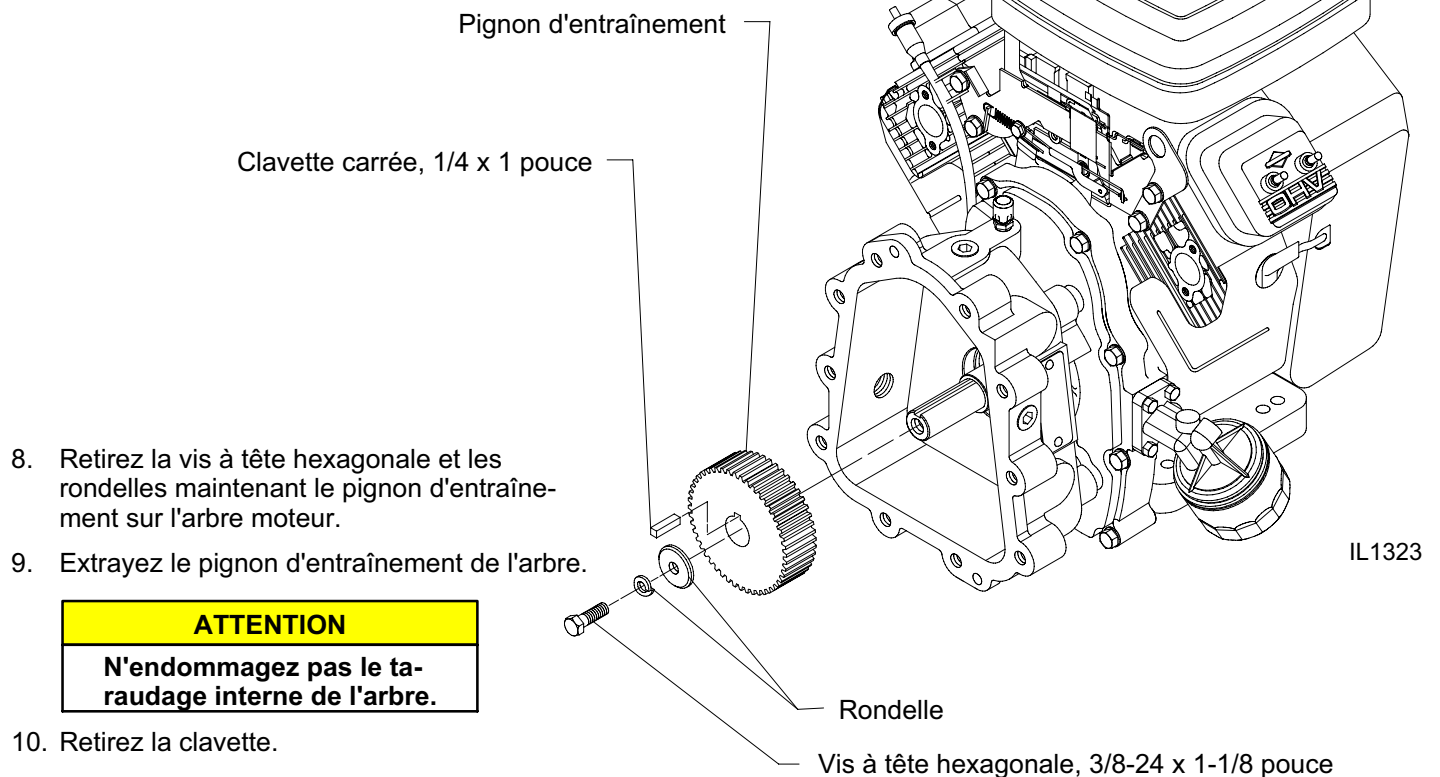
DÉPOSE DU CARTER D'ENGRENAGE
